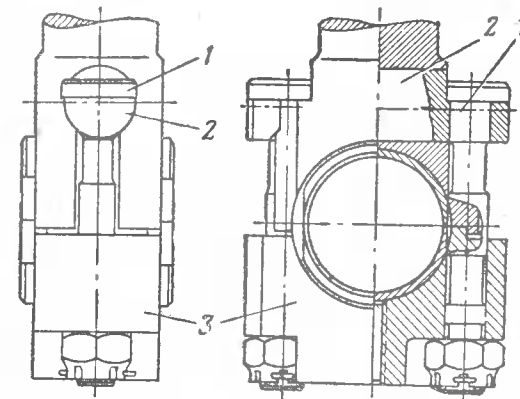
Трехцилиндровый трехступенчатый углеводородный компрессор ГН-10 и его основные детали.
